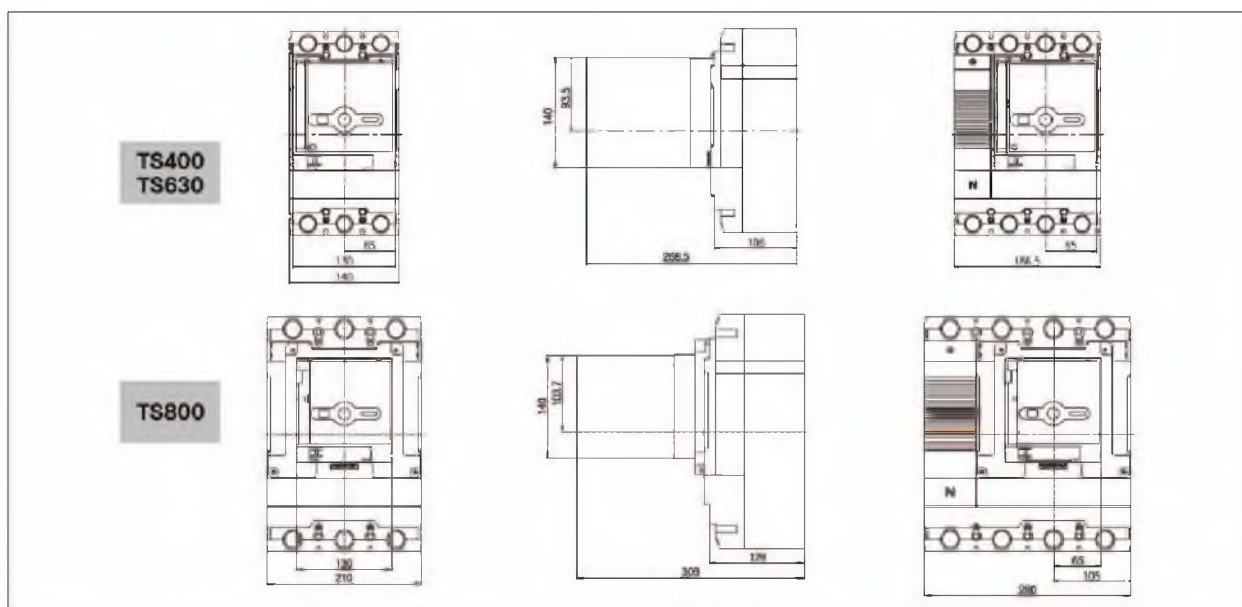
Габаритные размеры моторных приводов на выключатели TS400, TS630 и TS800
